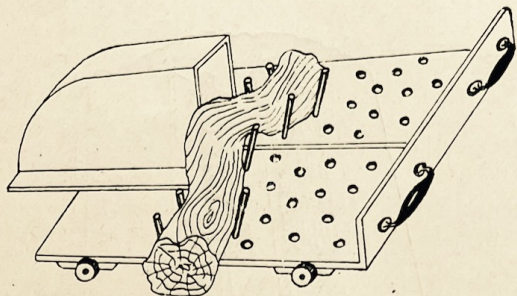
Još jedna vrsta naprave za potiskavanje
